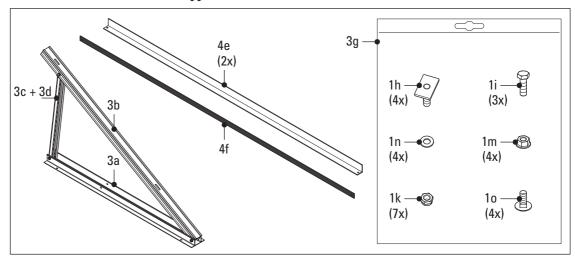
Struttura per tetto piano pacchetto di ampliamento FE H26P
